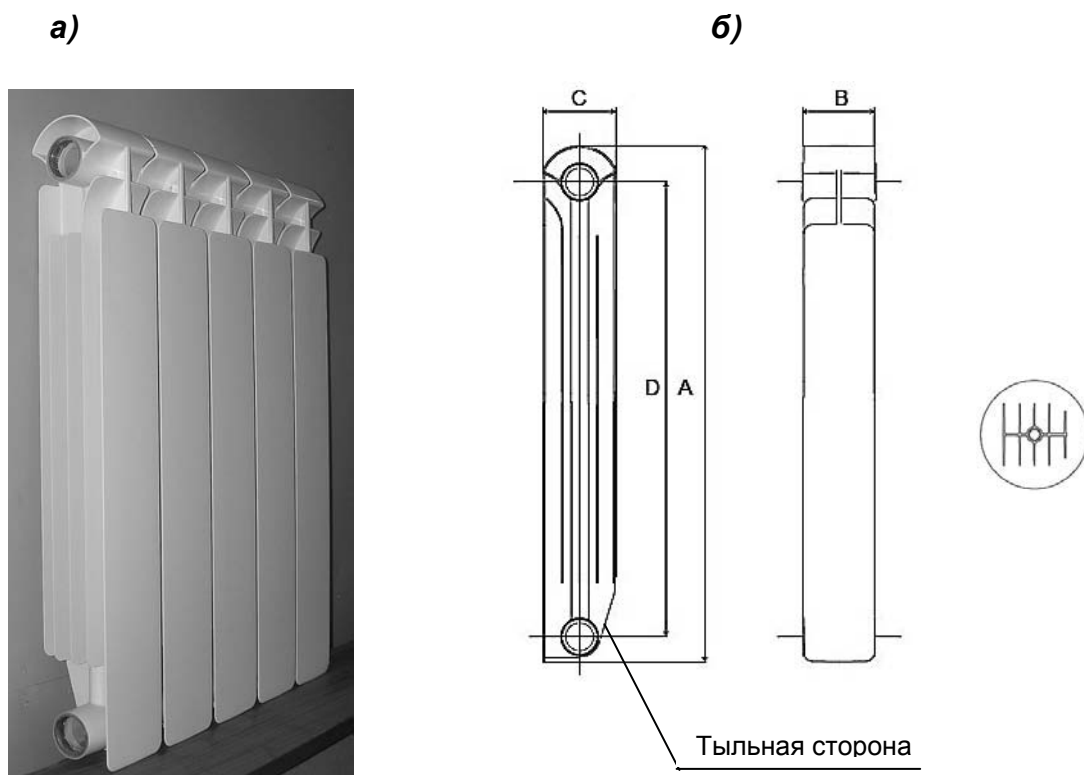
Общий вид (а) и габаритные размеры (б) биметаллического радиатора SFERA
